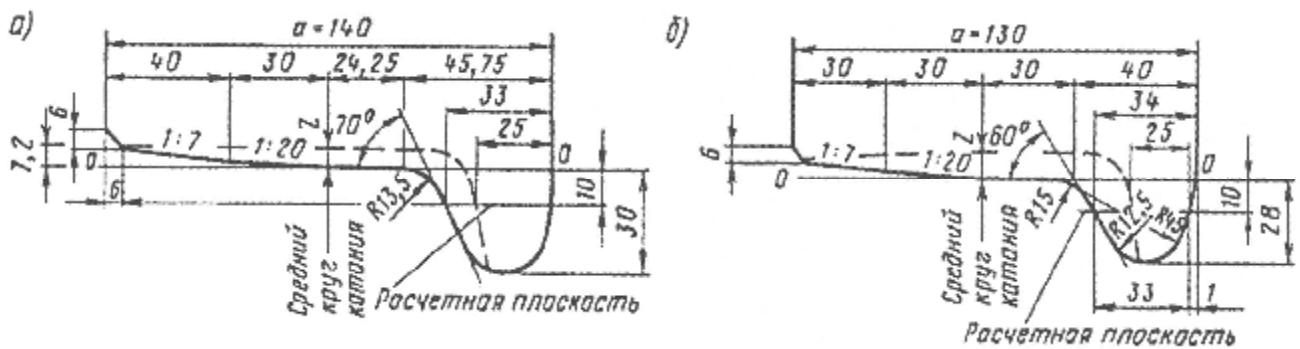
Очертание и основные размеры колес: а) – локомотивного; б) – вагонного (штриховой линией показаны предельные износы колес)
